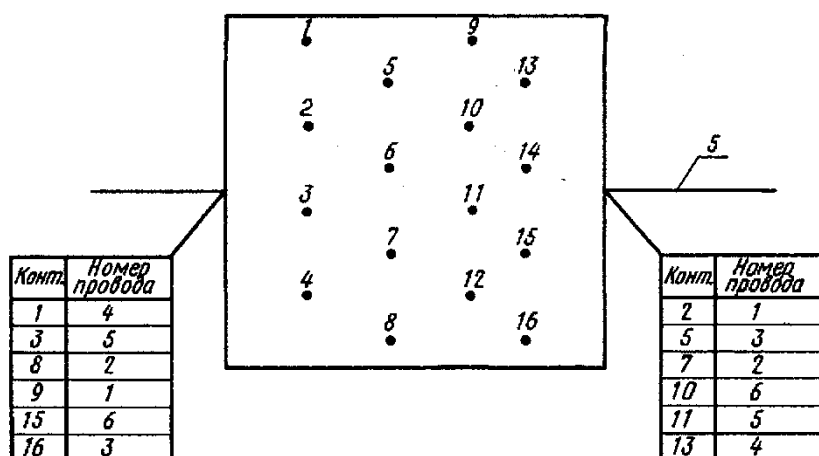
Схема присоединения проводов или жил кабеля
